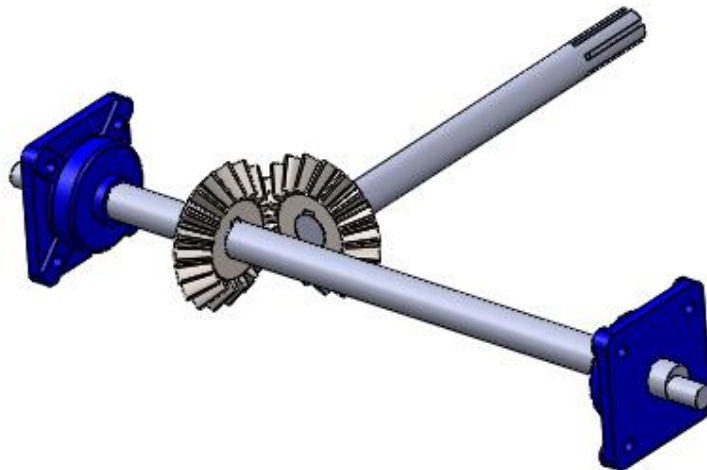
Vue en perspective du mécanisme de renvoi d'angle sur SolidWorks
